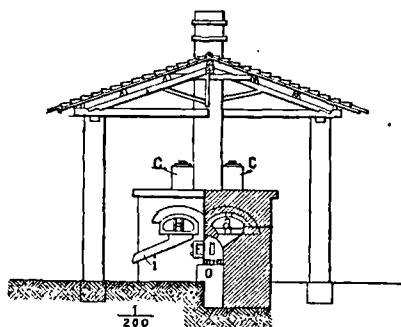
Four à mouffles de Rodriguez; vue de face.
